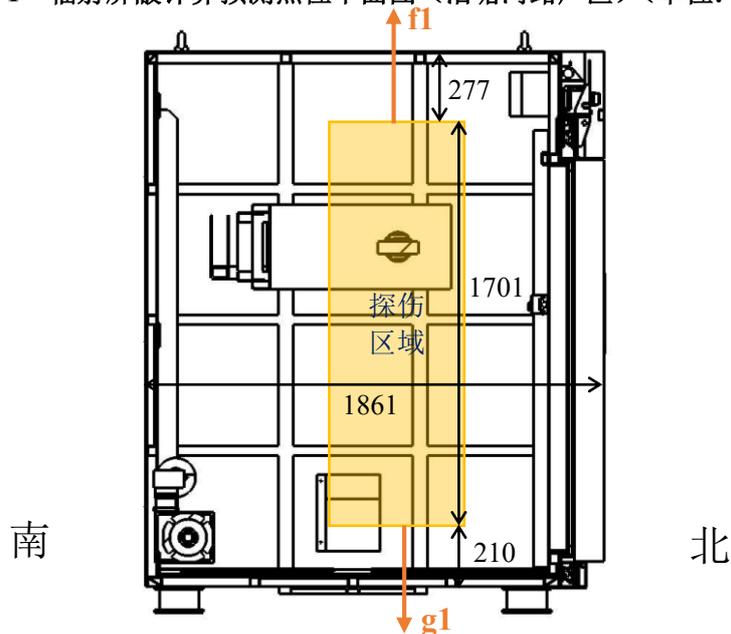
辐射屏蔽计算预测点位剖面图（沿塘河路厂区）（单位：mm）
